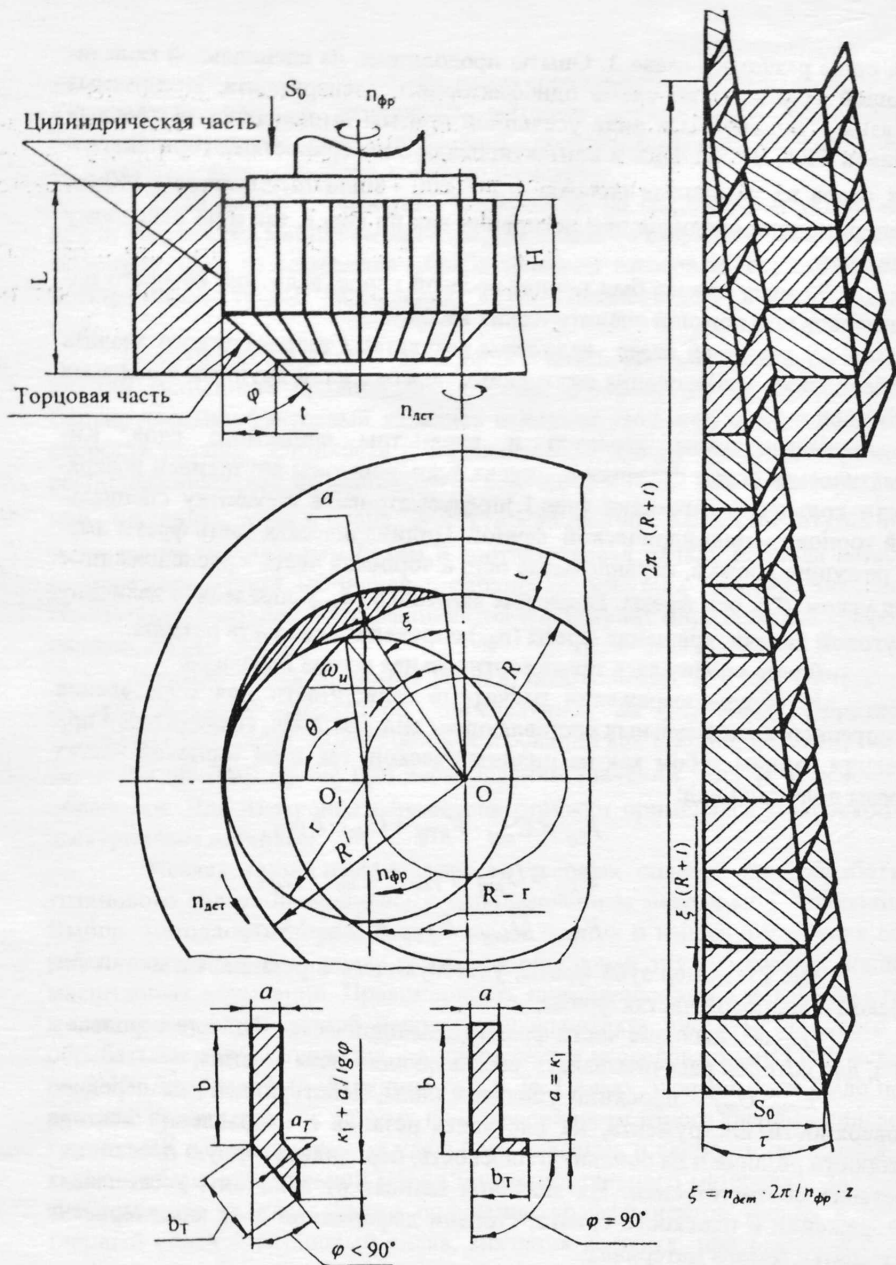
Схема обработки внутренней поверхности крупной кольцевой заготовки фрезерованием.
